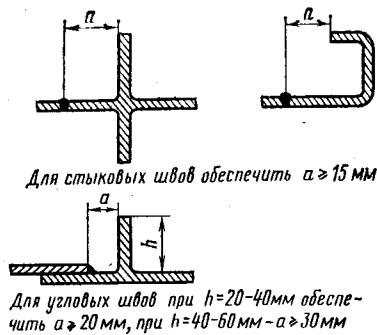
Пример конструктивного оформления сварного соединения с выступающими элементами, обеспечивающего выполнение сварки.
